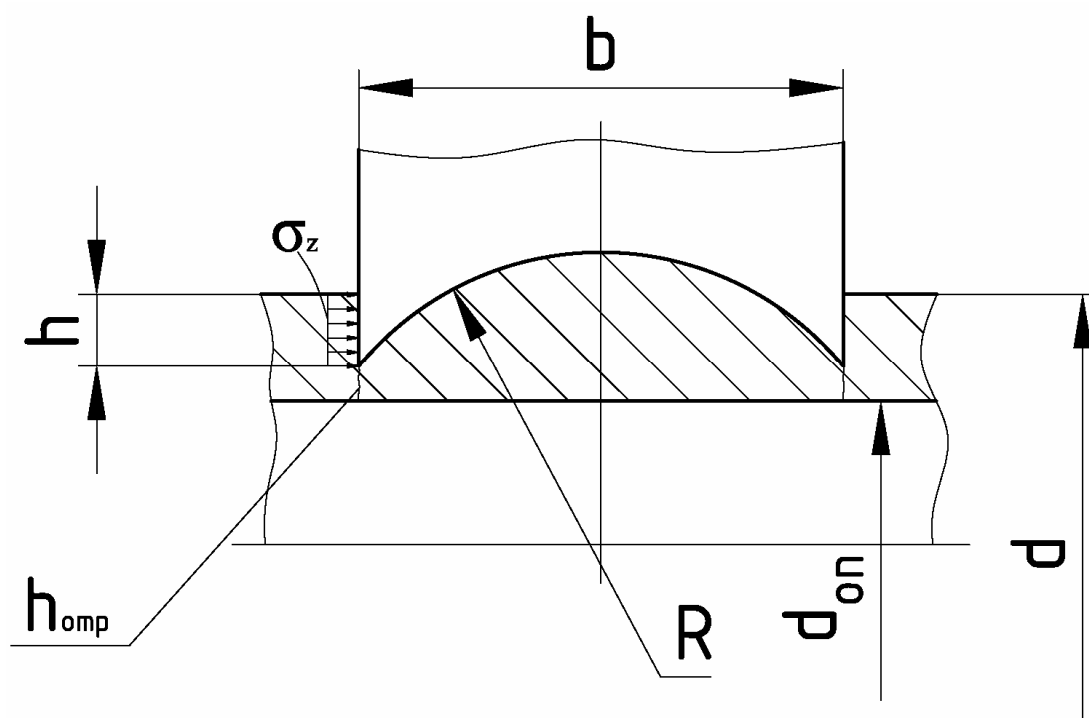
Принципиальная схема процесса поперечной прокатки шаровых втулок, предполагающая отрыв прокатываемой заготовки от основной части металла
